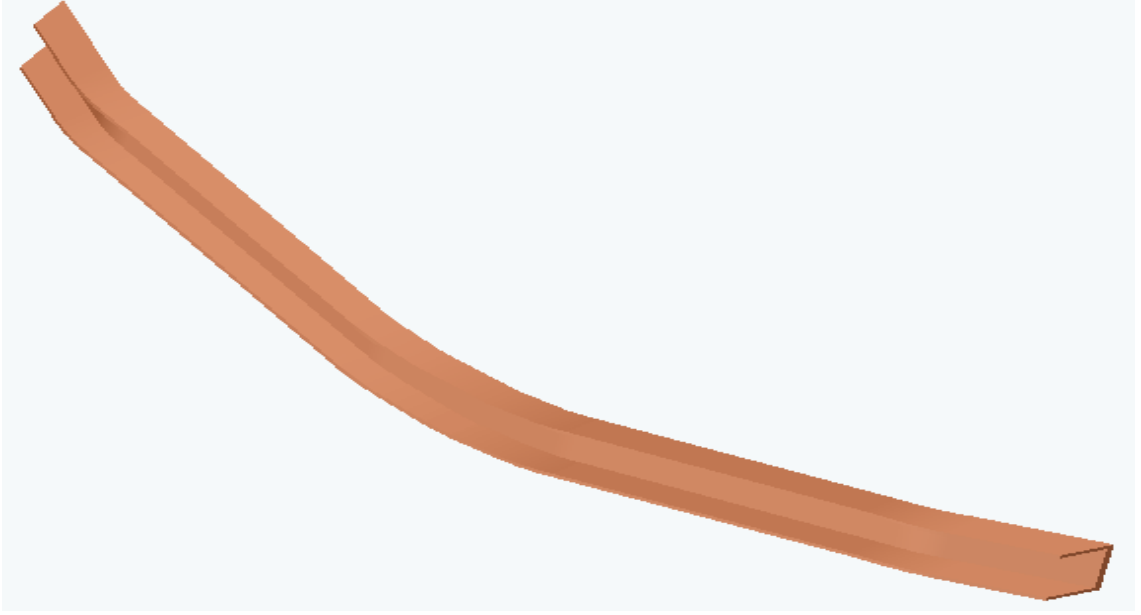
Yan Kiriş Üst Plakası Montajı
